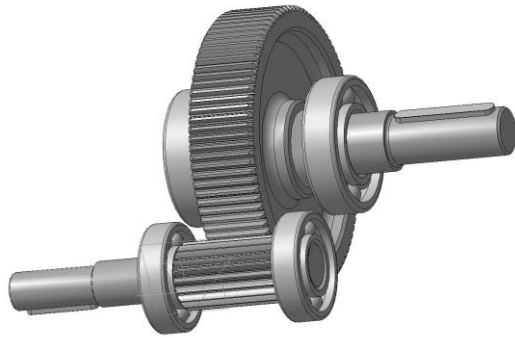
Загальний вид прямозубчастої циліндричної передачі
